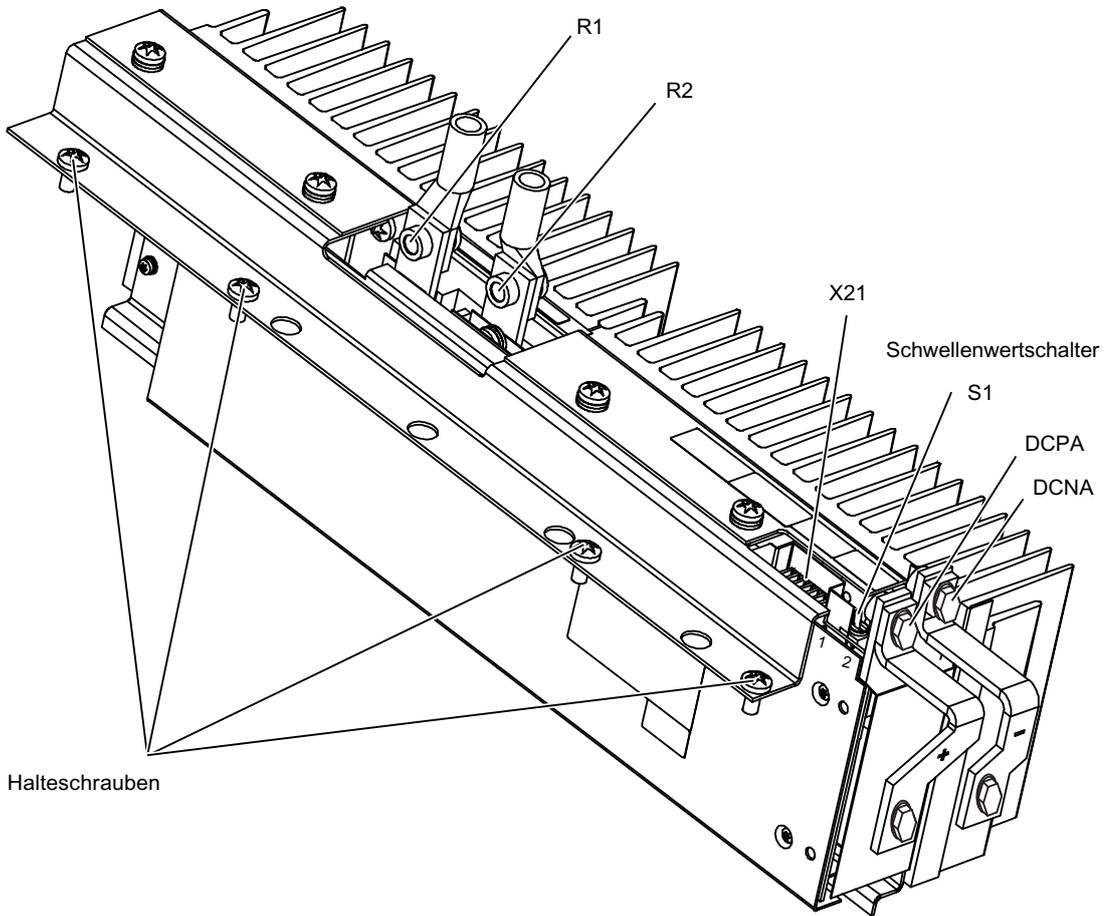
Braking Module für Power Module Baugröße HX / JX
